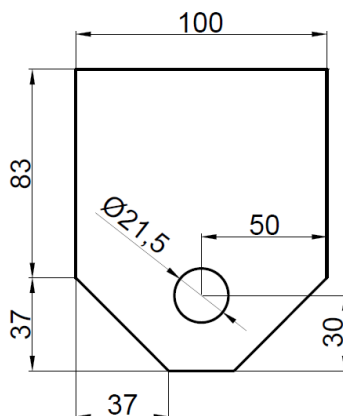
Detalle pieza de acero para la sujeción de las cadenas de aislamiento
